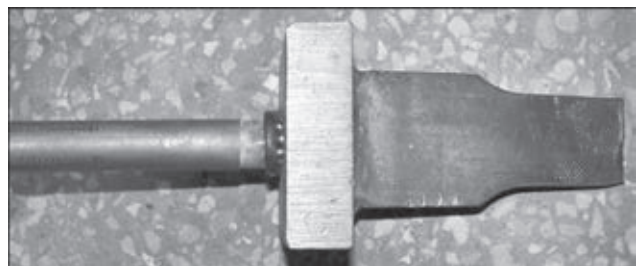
Общий вид сварного модельного образца для испытаний на усталость с призматической захватной частью
